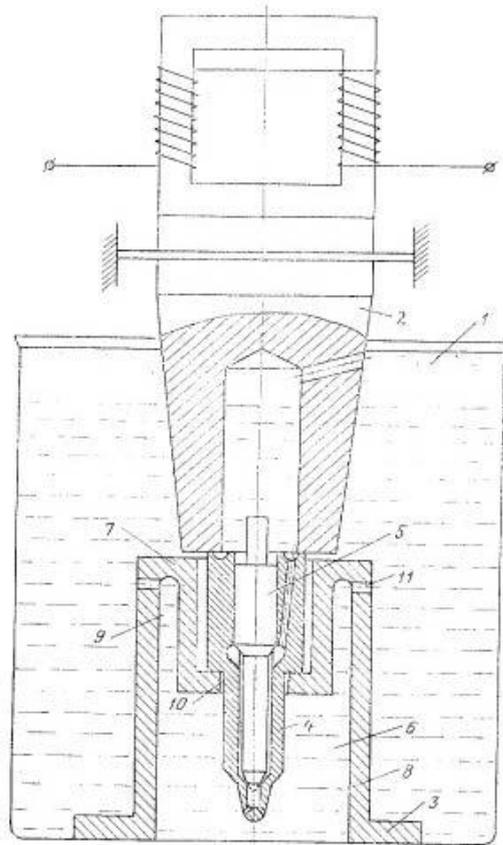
Патент № 659777. Устройство для разборки и очистки распылителя форсунки: 1- ванна с моющим раствором; 2- ультразвуковой преобразователь; 3- упор; 4- распылитель; 5- игла; 6- стакан; 7- ступенчатое днище стакана; 8- стенка стакана; 9- кольцевая полость; 10- центральное отверстие; 11- подпиточный канал.
